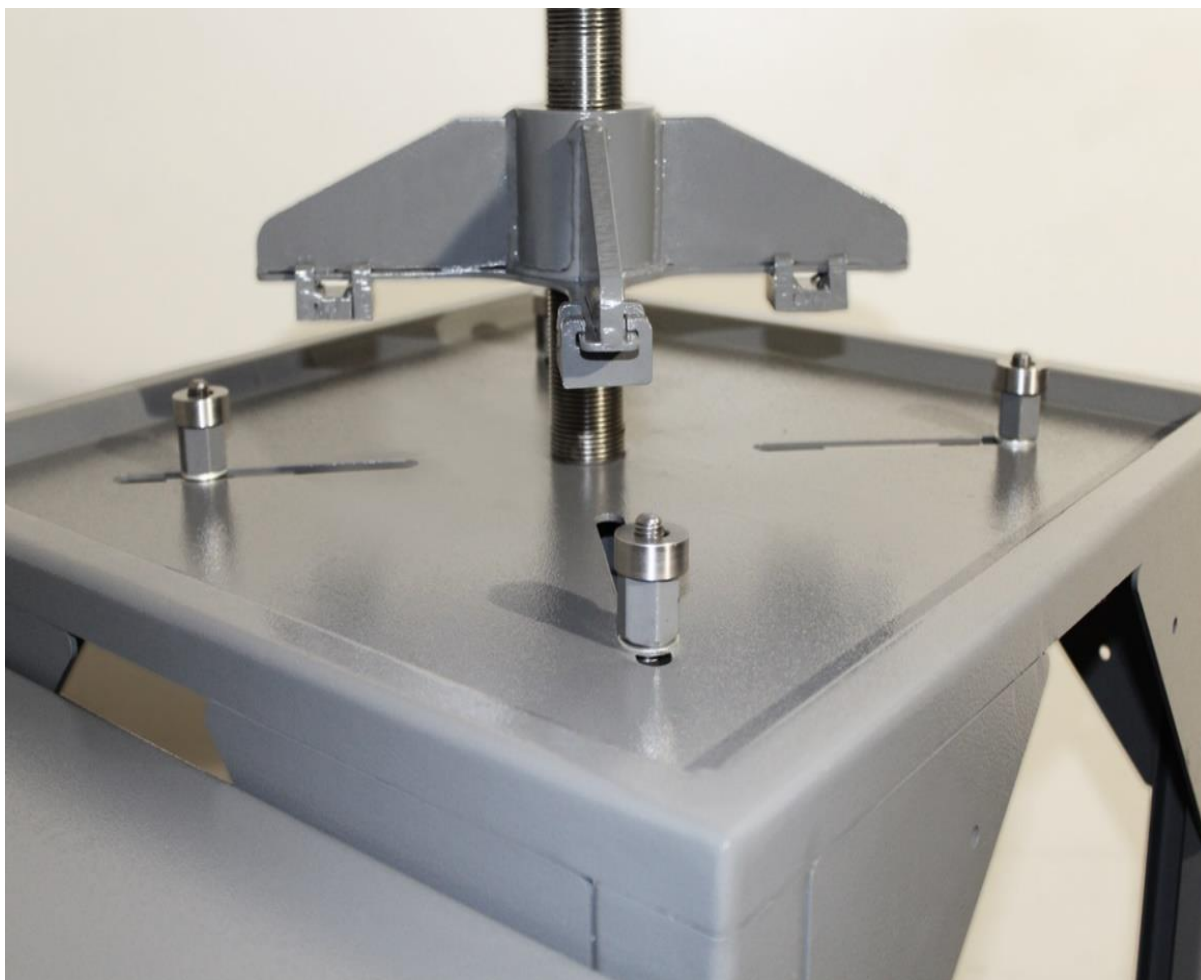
Стенд для сборки, регулировки, разборки сцепления
